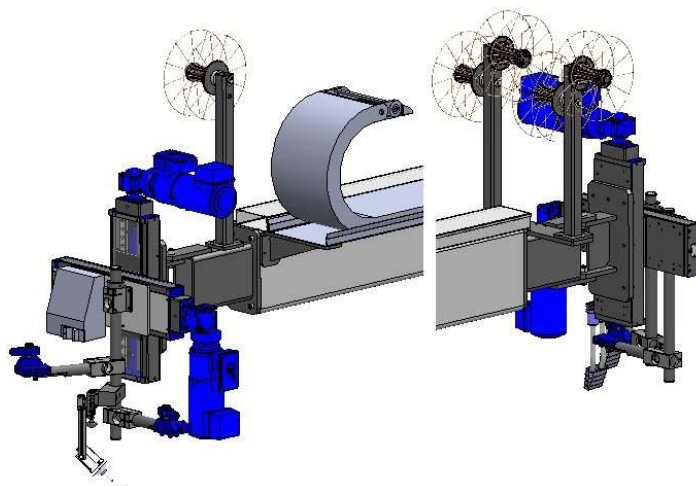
Cabeçal nos dois extremos na Coluna de Soldadura [24]
